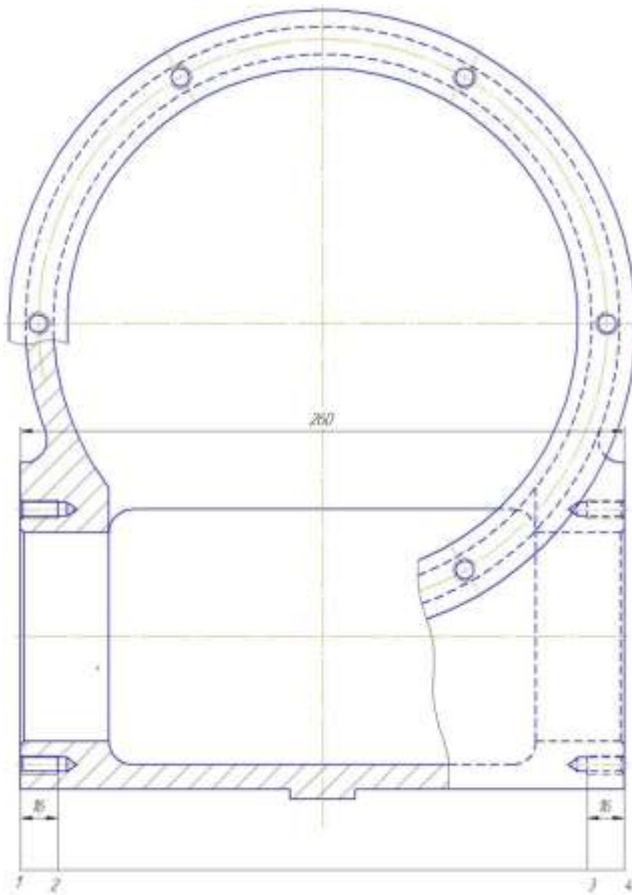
Преобразованный чертёж детали в первой проекции
